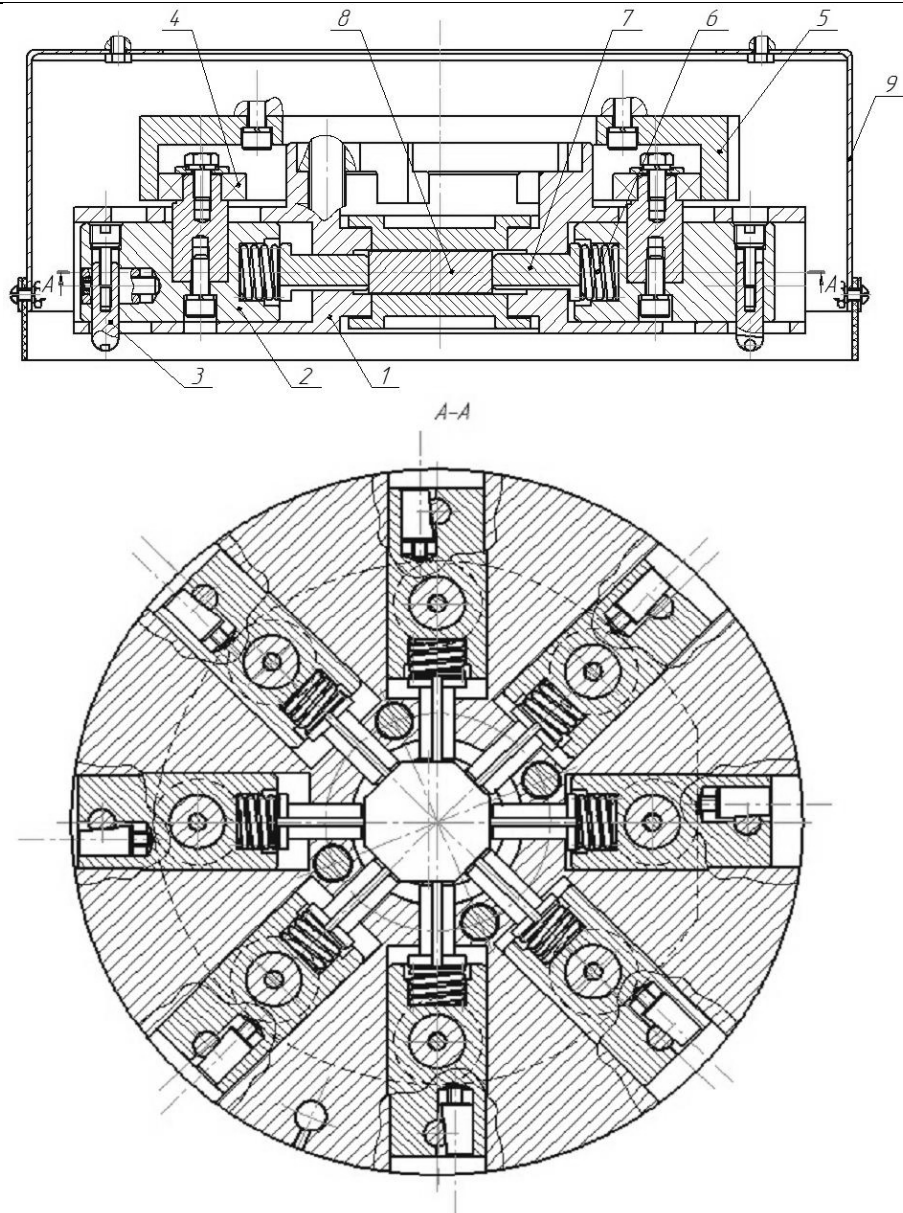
Загальний вигляд торцевого інструменту з кінематично перетворенням з колового у прямолінійний рухом формоутворюючих елементів. (Патент України №84478)
